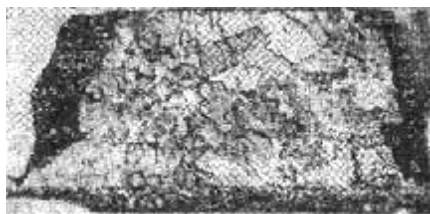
Нафталинистый излом быстрорежущей стали
